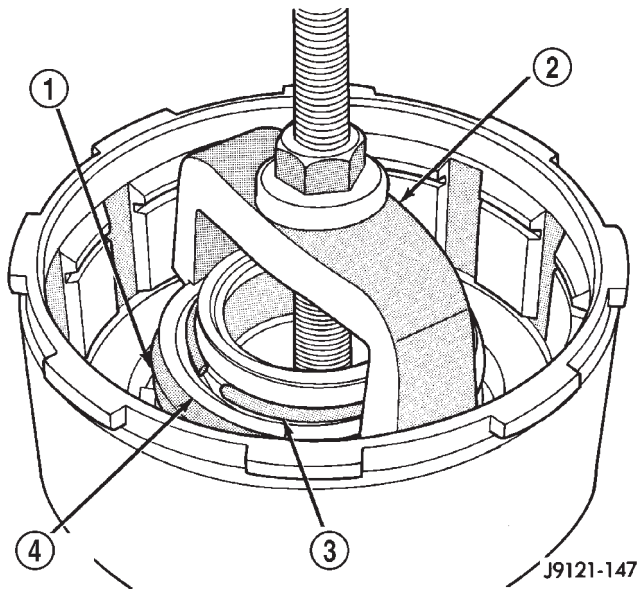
Compresión del muelle del émbolo del embrague delantero
